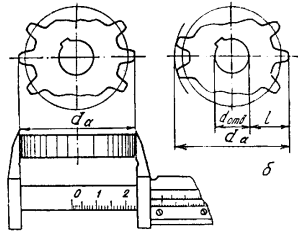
Схема вимірювання діаметра кола вершин і діаметра отвору під вал колеса
